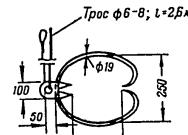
Кошка для крепления насадки к краю свай опоры.
